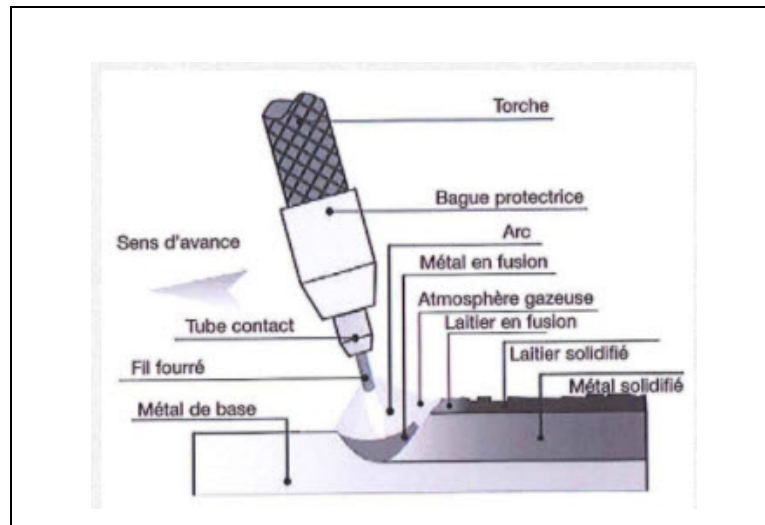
Procédé de soudage par fil fourré
